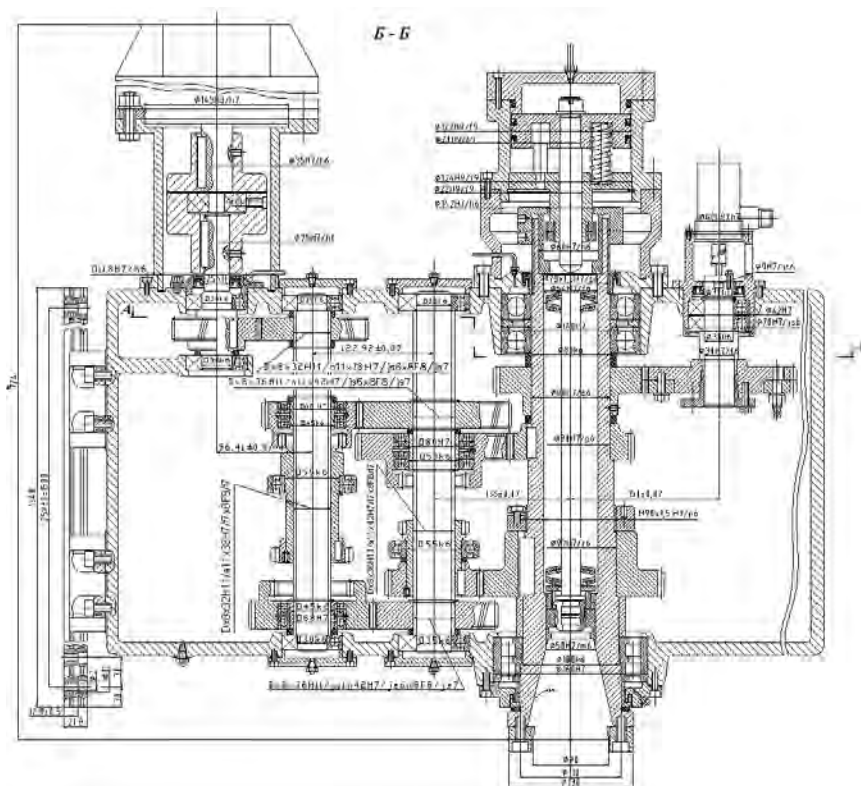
Шпиндельная бабка вертикального многооперационного сверлильно-фрезерно-расточного станка с ЧПУ
